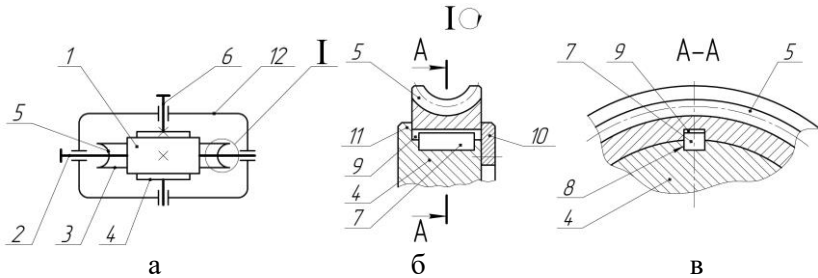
Черв'ячна передача: а – кінематична схема; б – фрагмент черв'ячного колеса; в – розріз А-А черв'ячного колеса
